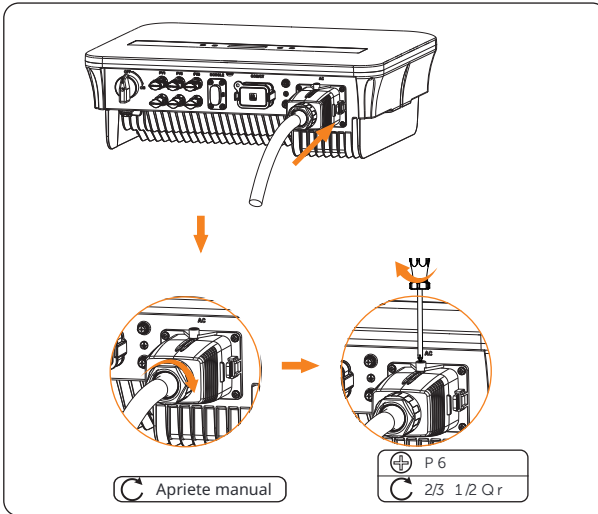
27 Fijación y aseguramiento de la cubierta impermeable de CA
